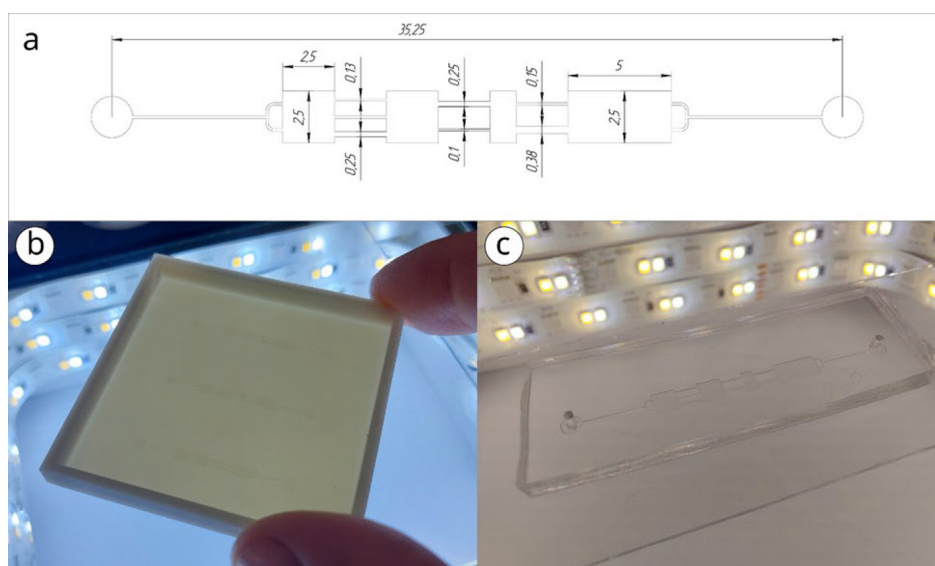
Чертеж (а), мастер-форма (b) и готовый образец (с) разработанного микрофлюидного чипа
